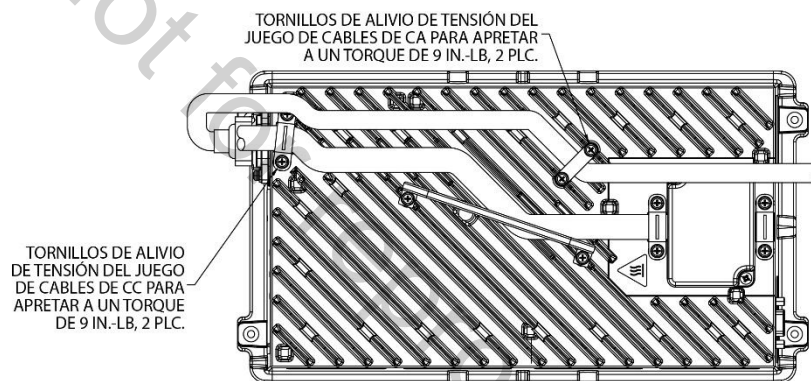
Recorrido alternativo del juego de cables de CA y CC
